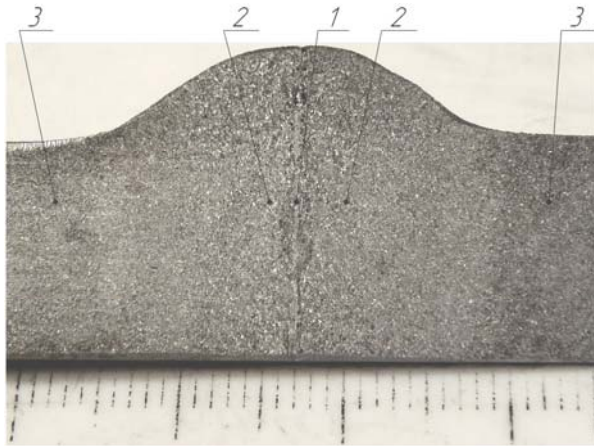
Макроструктура сварной заготовки титана типа ВТ1-0, полученного методом ПМ:
